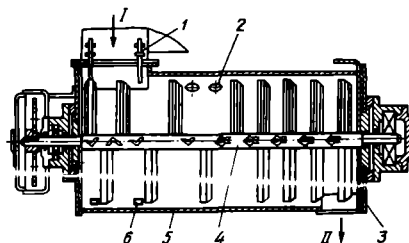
Смеситель пресс-гранулятора ДГ-1:
